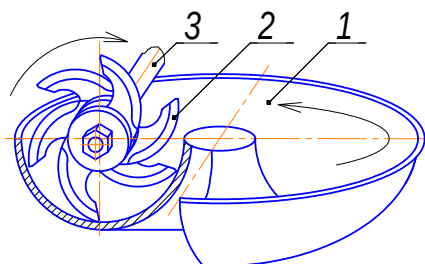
Принципова схема кутера: 1 – чаша; 2 – ножова головка; 3 – ножовий вал
